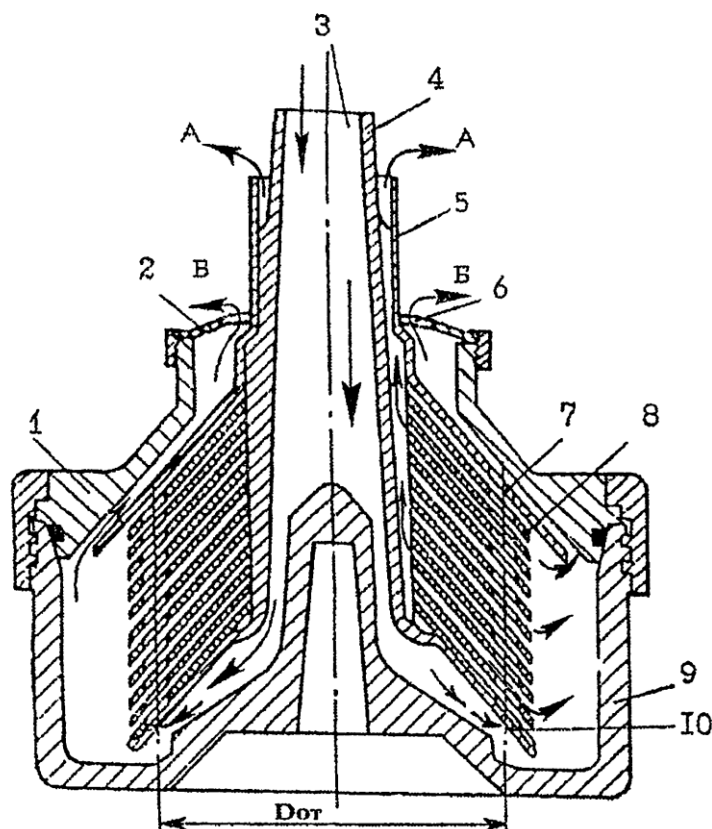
Схема барабана – пурификатора: 1 – крышка барабана; 2 – регулировочная шайба; 3 – центральный канал; 4 – тарелкодержатель; 5 – патрубок для выхода топлива; 6 – отверстие в регулировочной шайбе; 7 – разделительная тарелка; 8 – тарелки сепаратора; 9 – барабан; 10 – отверстия в нижней тарелке
